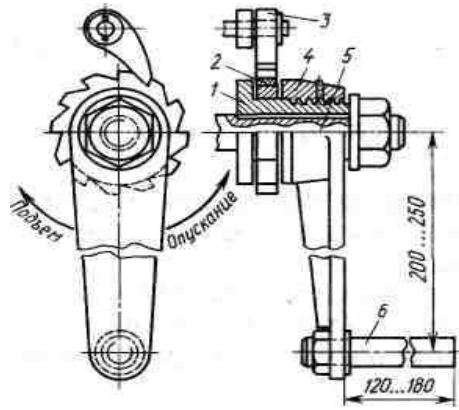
Схема безпечної рукоятки лебідки
